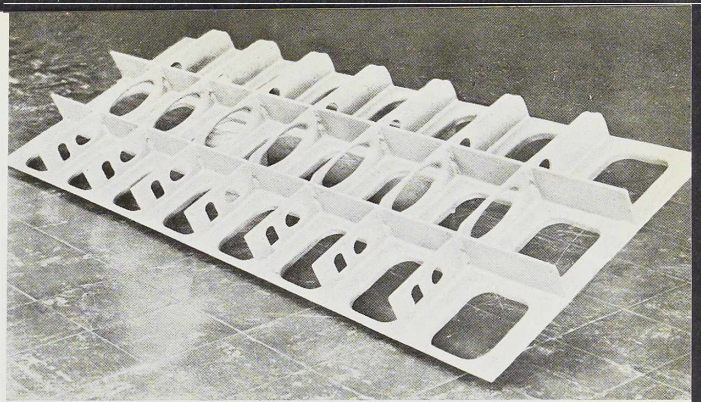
Application de pièces forgées à la constitution d'éléments soudés de forme irrégulière.
